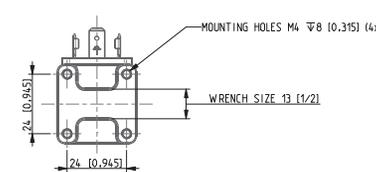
Dimensions 1/8" en ligne, largeur de la bobine
